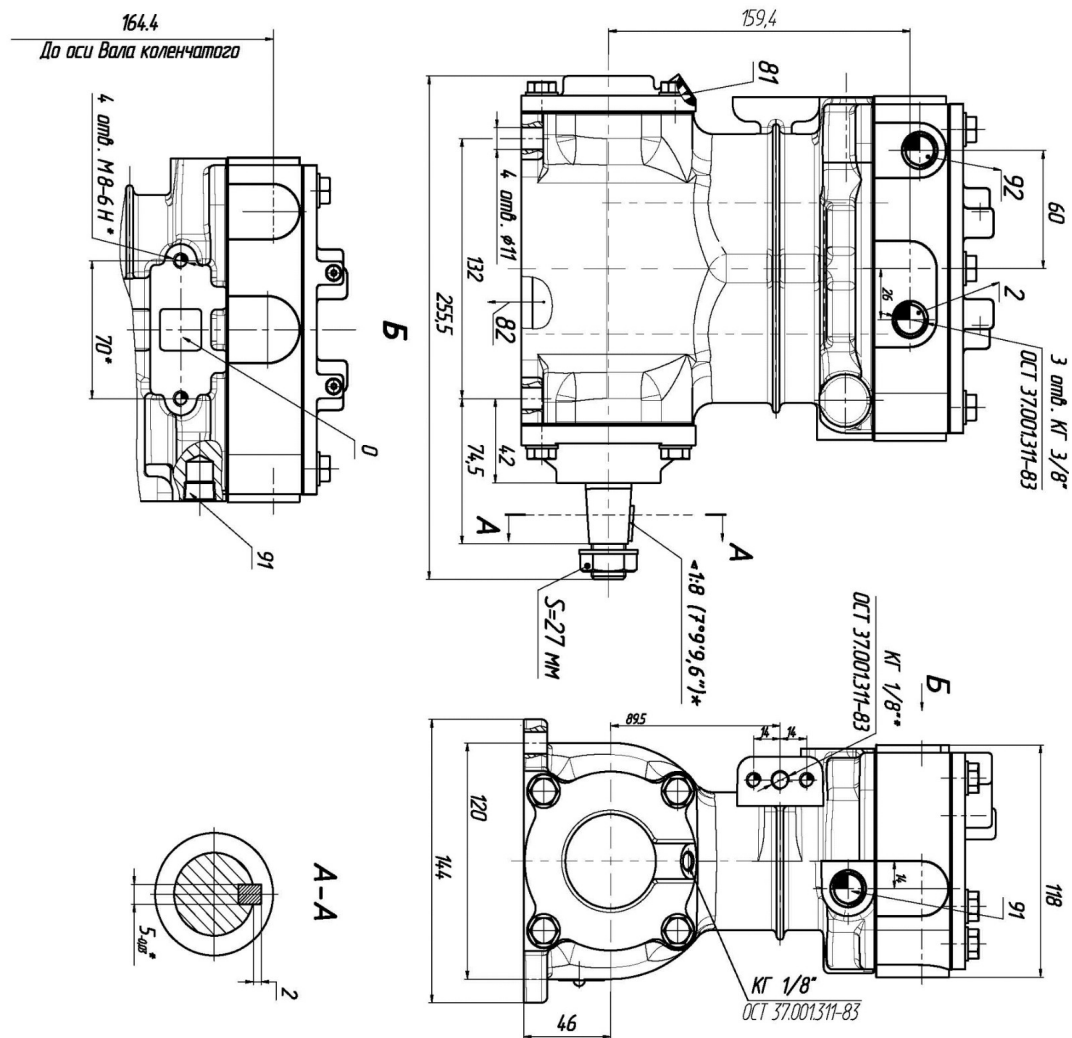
Присоединительные и установочные размеры компрессора
